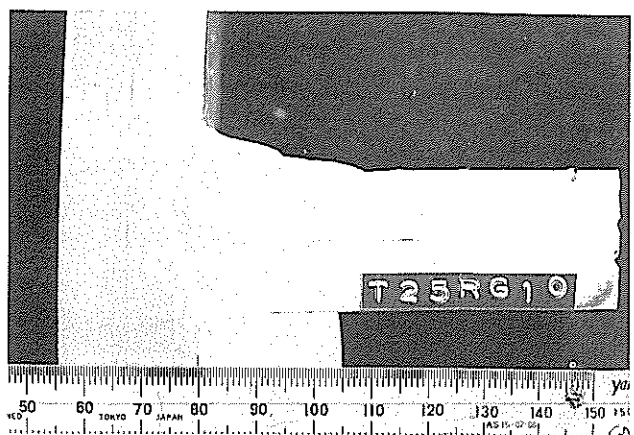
25mm厚レ型溶接部のマクロ断面
